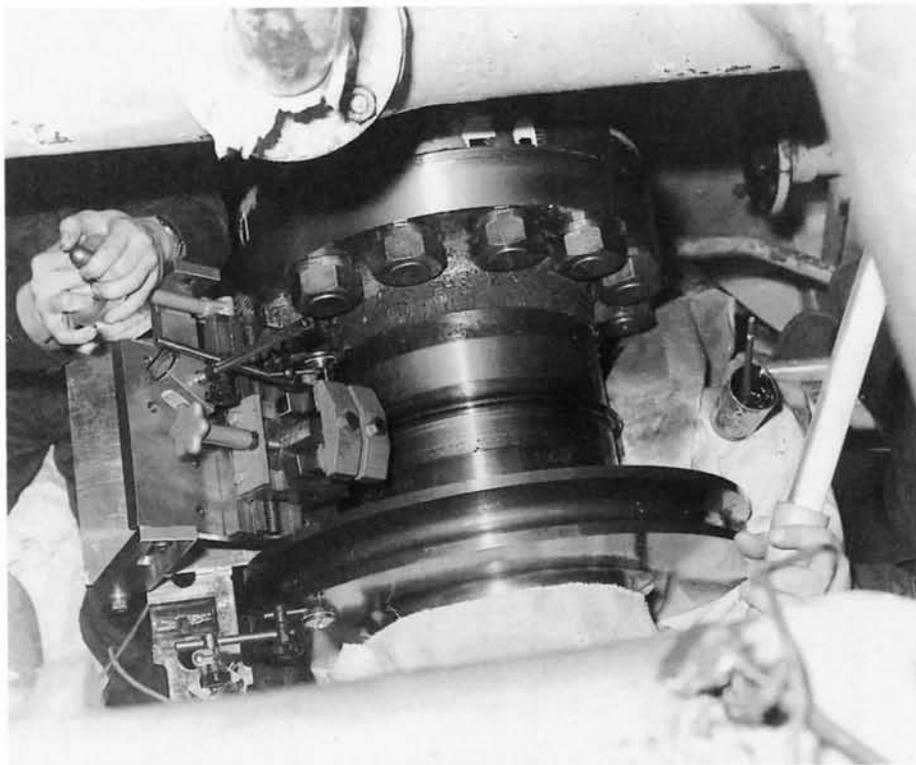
Usinage de l'arbre de butée du carter d'engrenages sur place.
